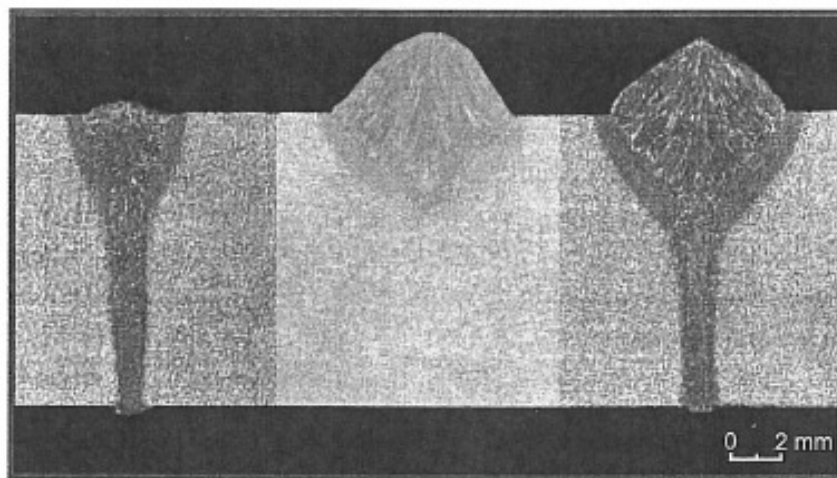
Typische Schweißnähte für die jeweiligen Prozesse; links: Laserstrahlschweißen; Mitte: MSG-Schweißen; rechts: Hybridschweißen [15]
